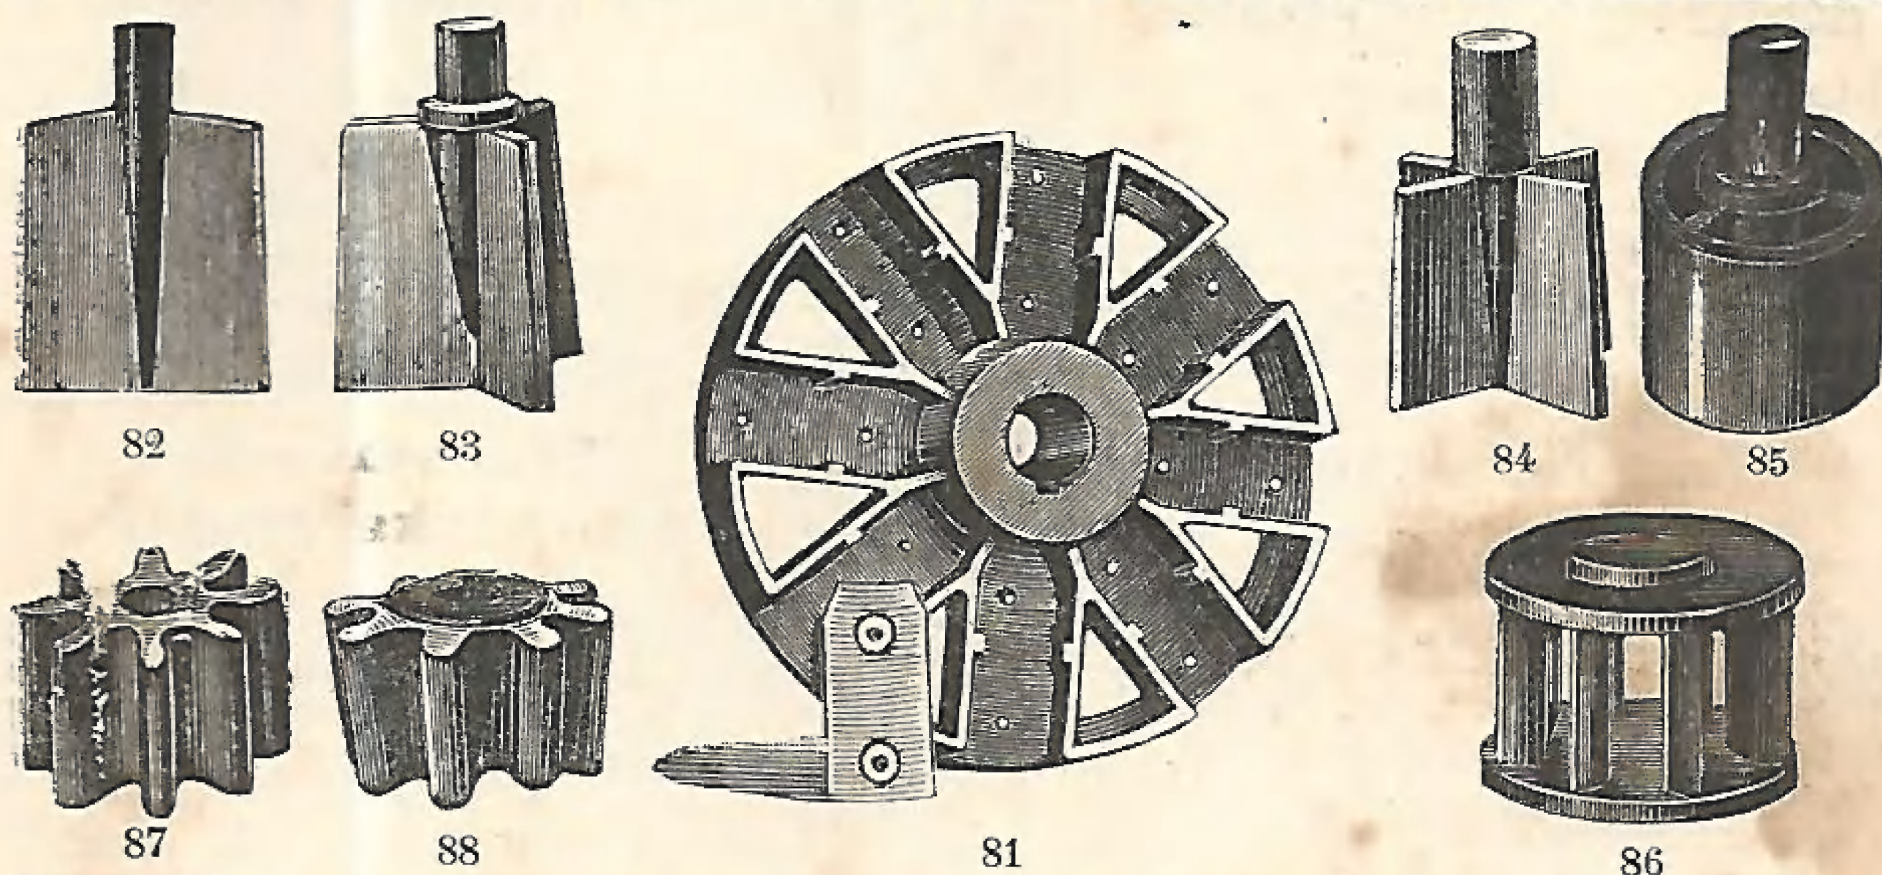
Wasserrad-Rosetten sammt Platten und Schrauben für Wasserräder mit Stahlachsen, auch für solche mit Holz und schmiedeisernen Armen.
